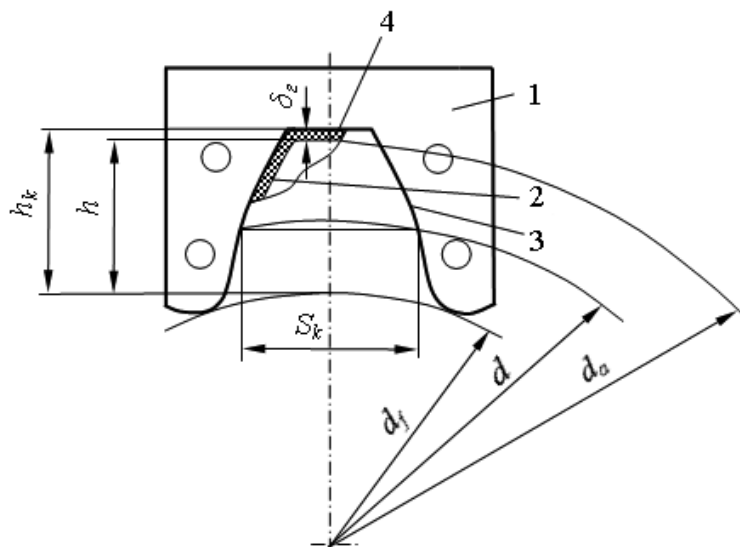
Схема профиля рабочей поверхности кристаллизатора: 1 – кристаллизатор; 2 – расчётный эвольвентный профиль зуба; 3 – профиль рабочей поверхности кристаллизатора; 4 – гарнисажная корочка;  $d$  – делительный диаметр;  $d_a$  – диаметр вершин зубьев;  $d_f$  – диаметр впадин;  $h$  – расчётная высота восстанавливаемого зуба;  $h_k$  – высота профиля полости кристаллизатора;  $\delta_z$  – толщина гарнисажной корочки;  $S_k$  – ширина формирующей полости по хорде делительной окружности.
